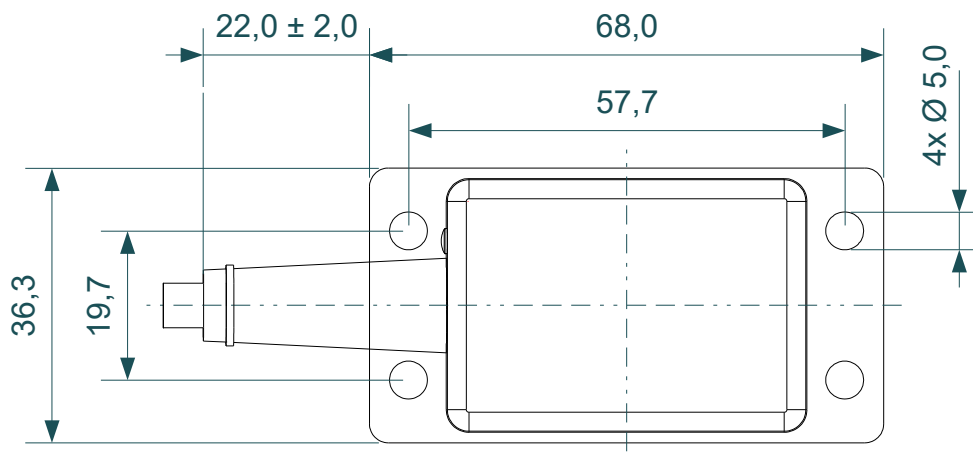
Befestigungsbohrungen kleines Kunststoffgehäuse (SP) mit Kabel (Maße in mm)
